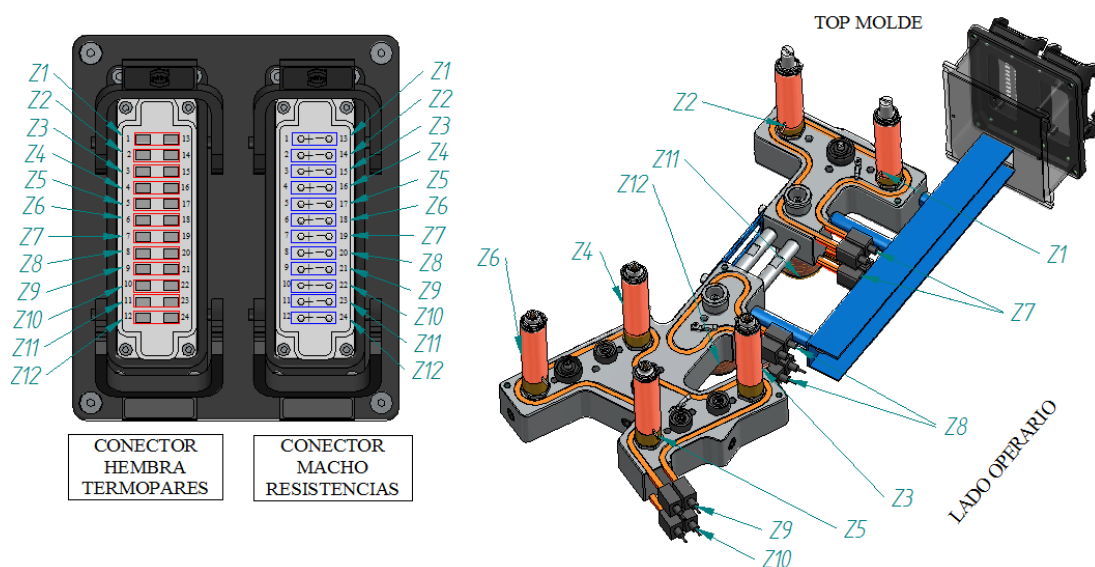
Detalle de conexionado del sistema de Cámara Caliente
